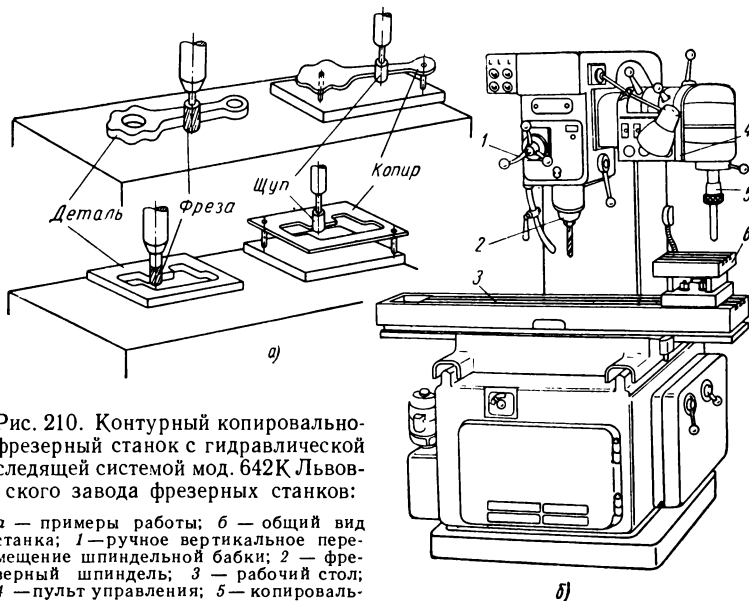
Контурный копировально-фрезерный станок с гидравлической следящей системой мод. 642К Львовского завода фрезерных станков:
